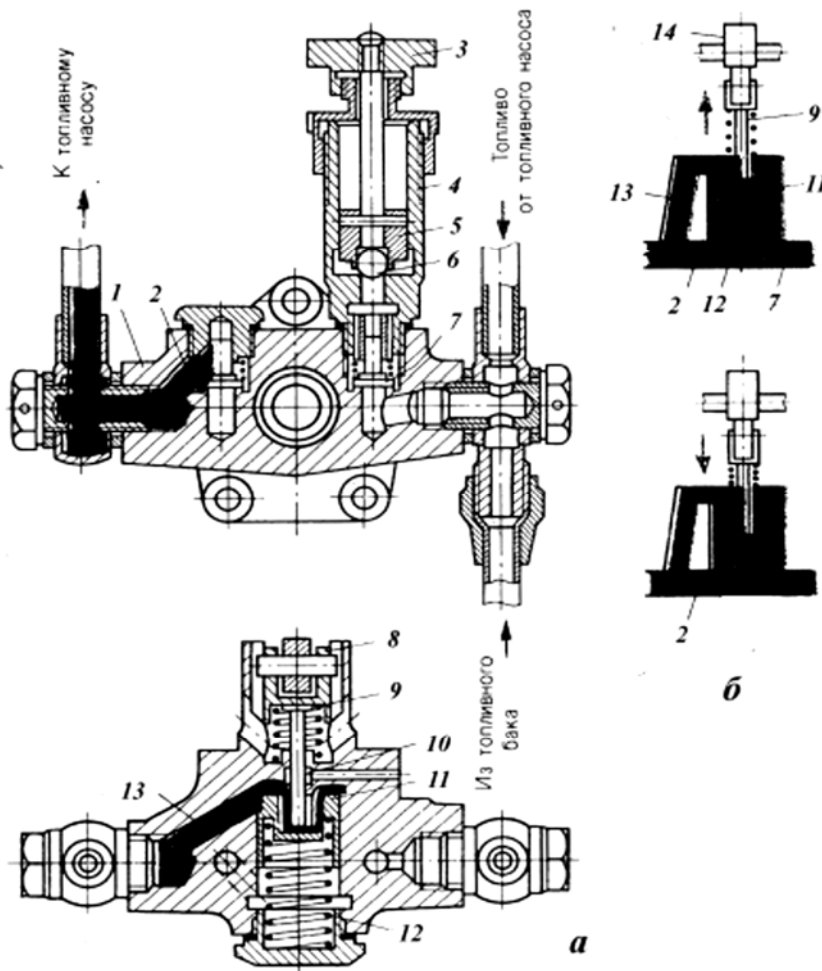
Универсальный поршневой топливоподкачивающий насос:
